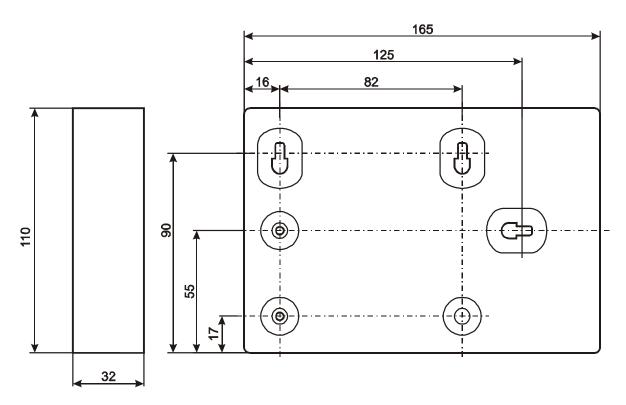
Габаритные и присоединительные размеры КД2 (исполнение IP20)
